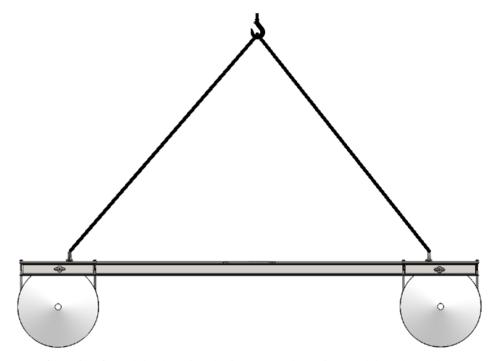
Vista frontal de elevación de sistema emplazamiento. Elaborado por los autores.
